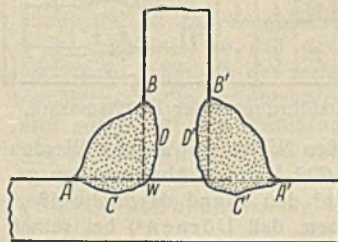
Ohne Vorschweißen mit dünnen Schweißdrähten zu tiefer Einbrand in den Nahtschenkeln.
